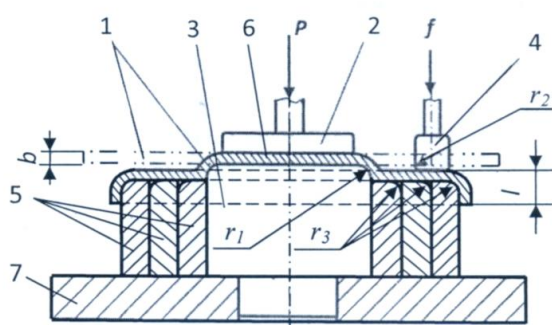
Многопереходная обкатка при изготовлении полых деталей: 1- деформируемая листовая заготовка; 2- прижимное устройство; 3- оправка; 4- деформирующий ролик; 5- удаляемые по переходам технологические цилиндры; 6- донная часть заготовки; 7- корпус
